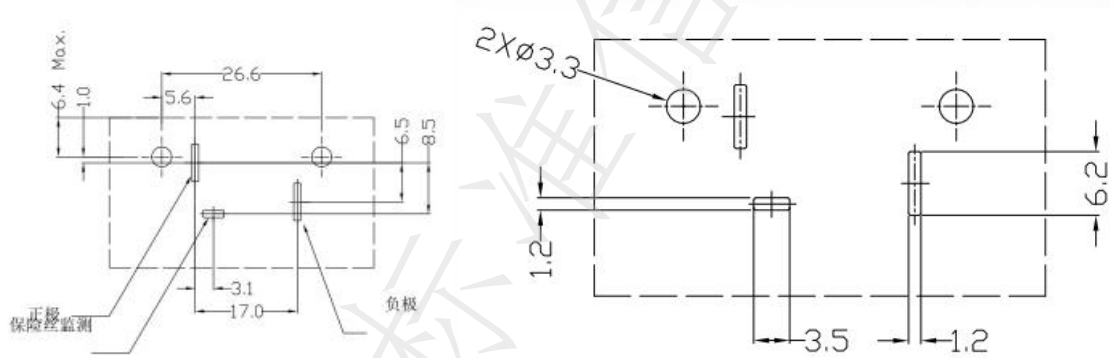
PCB 开孔尺寸 (厚度 2.0mm)
